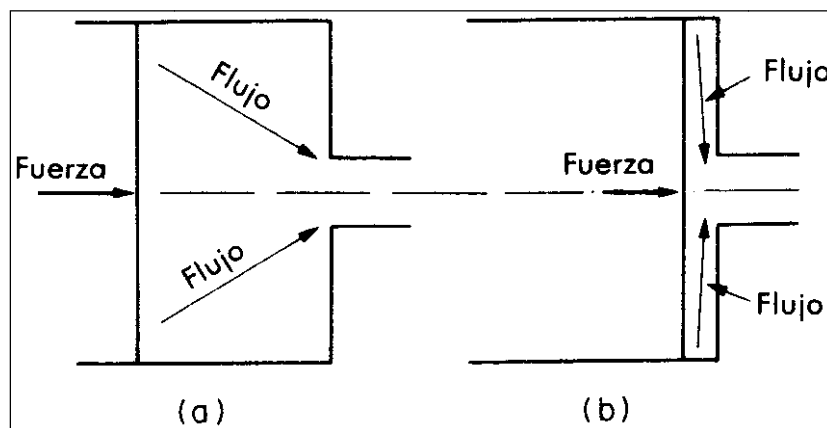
Esquema del flujo y la fuerza en un proceso de extrusión.
